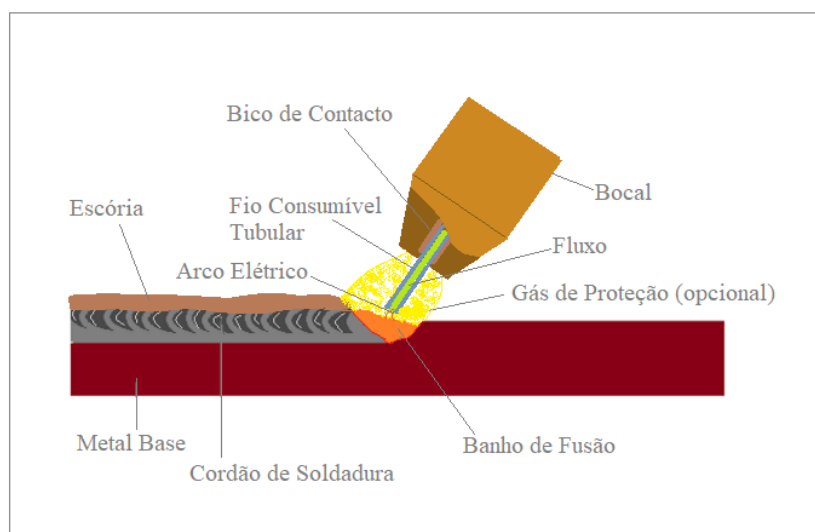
Ilustração da soldadura por fio fluxado (FCAW) – [10] Imagem adaptada
